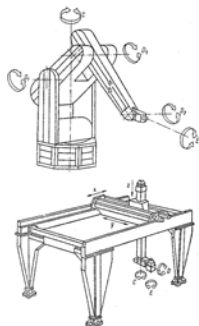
Зварювальний робот фірми «Німак» (Німеччина)
